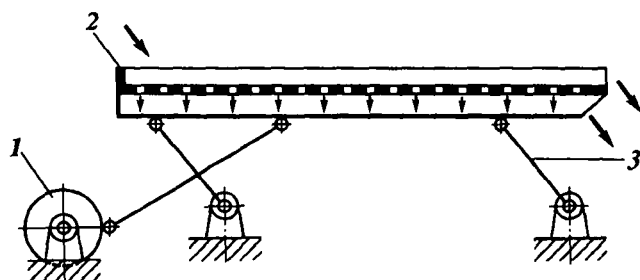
Схема качающегося грохота: 1 — эксцентрик; 2 — корпус; 3 — опорная стойка
